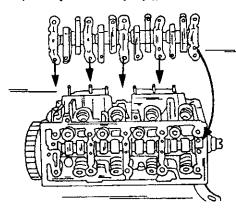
Установка вала коромысел. Стрелками указано положение центрирующих штифтов.
